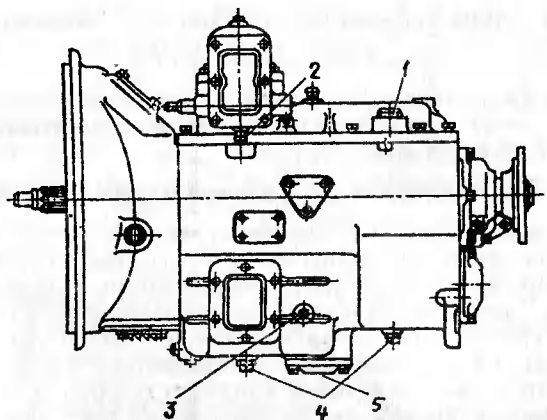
Пробки и крышка на коробке передач ЯМЗ-236П:
